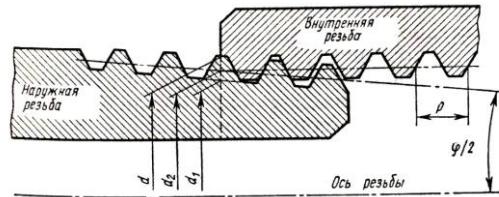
Цилиндрическое резьбовое соединение
